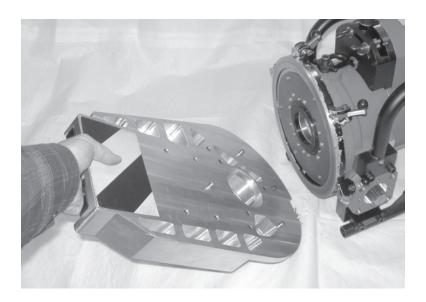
Демонтируйте однорезцовый суппорт.
